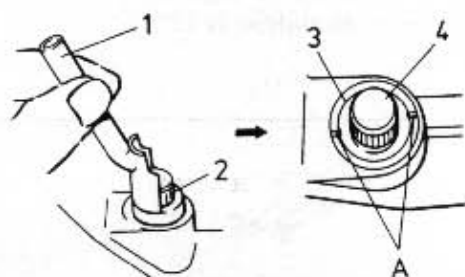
DEMONTAŻ ZEWNĘTRZNEJ TULEJKI ŁOŻYSKUJĄCEJ WAŁEK WYŁĄCZAJĄCY SPRZĘGŁO
